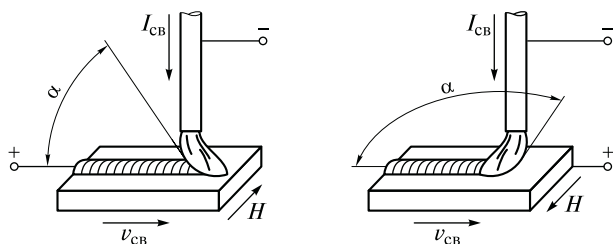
Отклонения столба дуги под действием магнитного поля при сварке:
